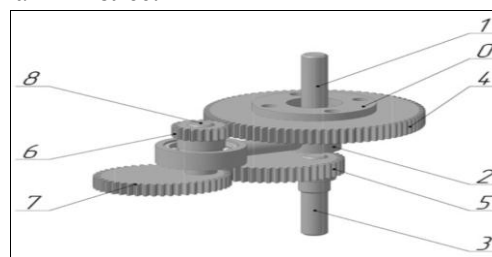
Планетарный механизм с прямозубыми и эллиптическими шестернями.
